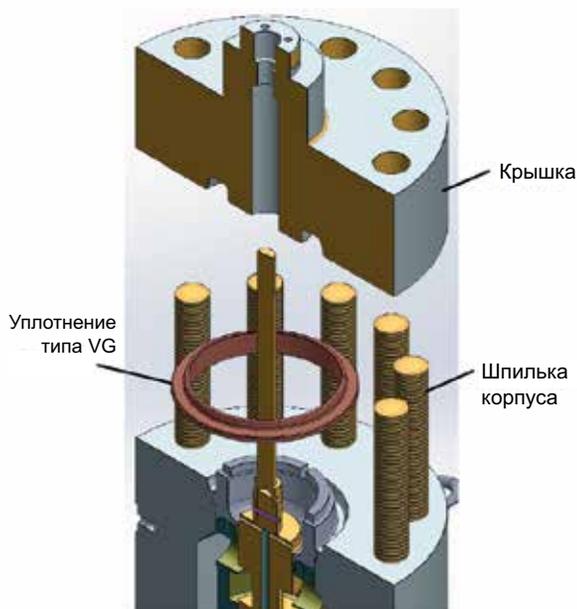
Компонувку уплотнения VG и крышки корпуса
